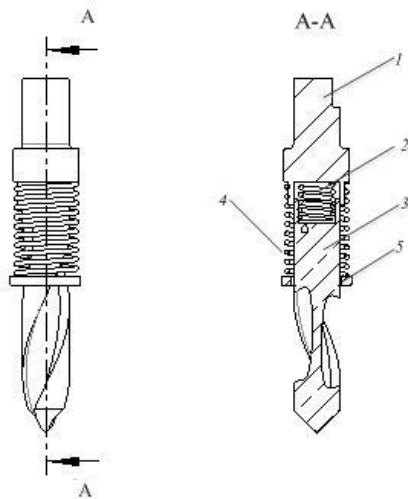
Сверло сборное для сверления ЛДСтП: 1- хвостовик, 2 - внутренний упругий элемент, 3 - режущая часть, 4 - внешний упругий элемент, 5- предохранительный элемент (шайба)
